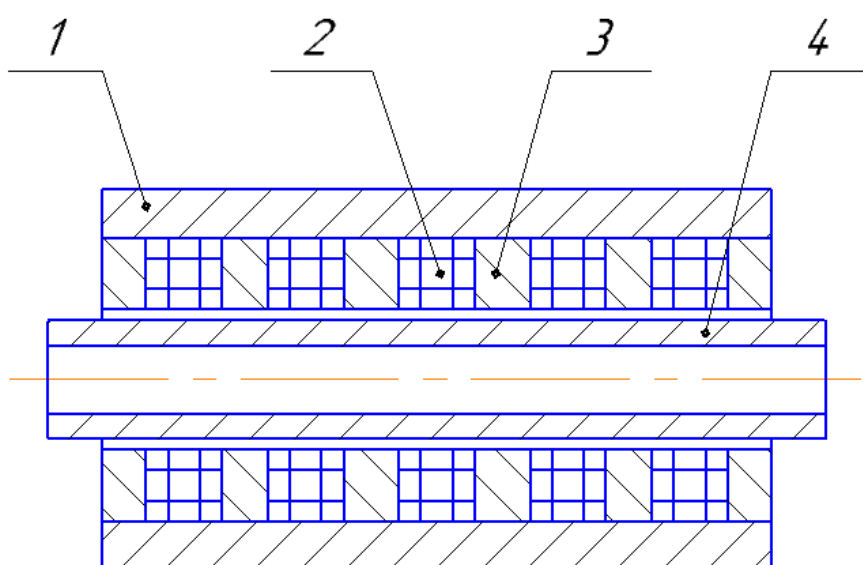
Линейный двигатель цилиндрической конструкции:
